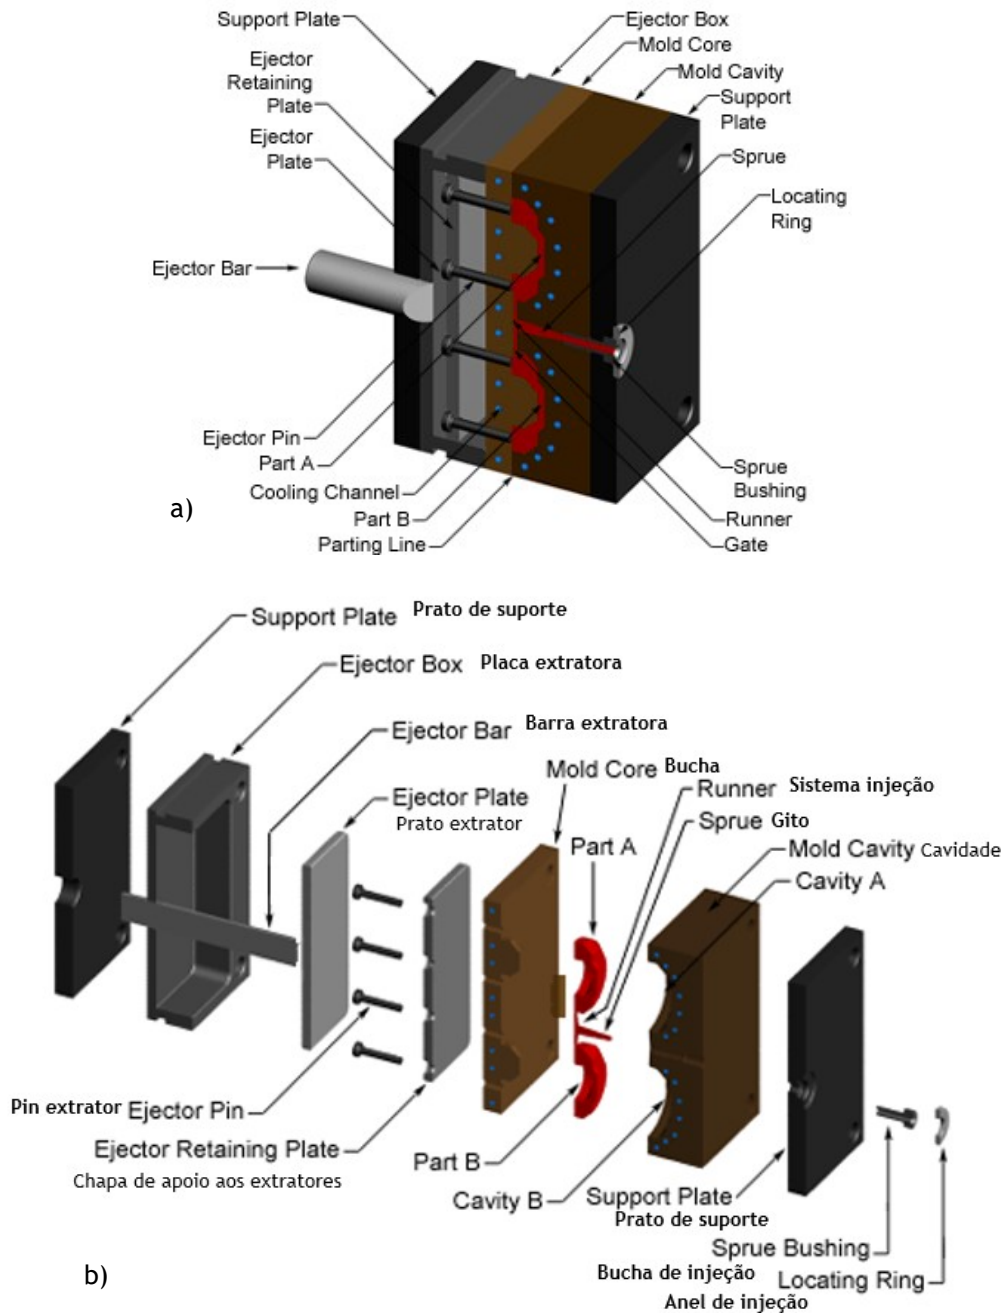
Constituição de um molde de duas cavidades. a) Molde fechado com todos os seus componentes. b) Componentes do molde em vista explodida. [27]
